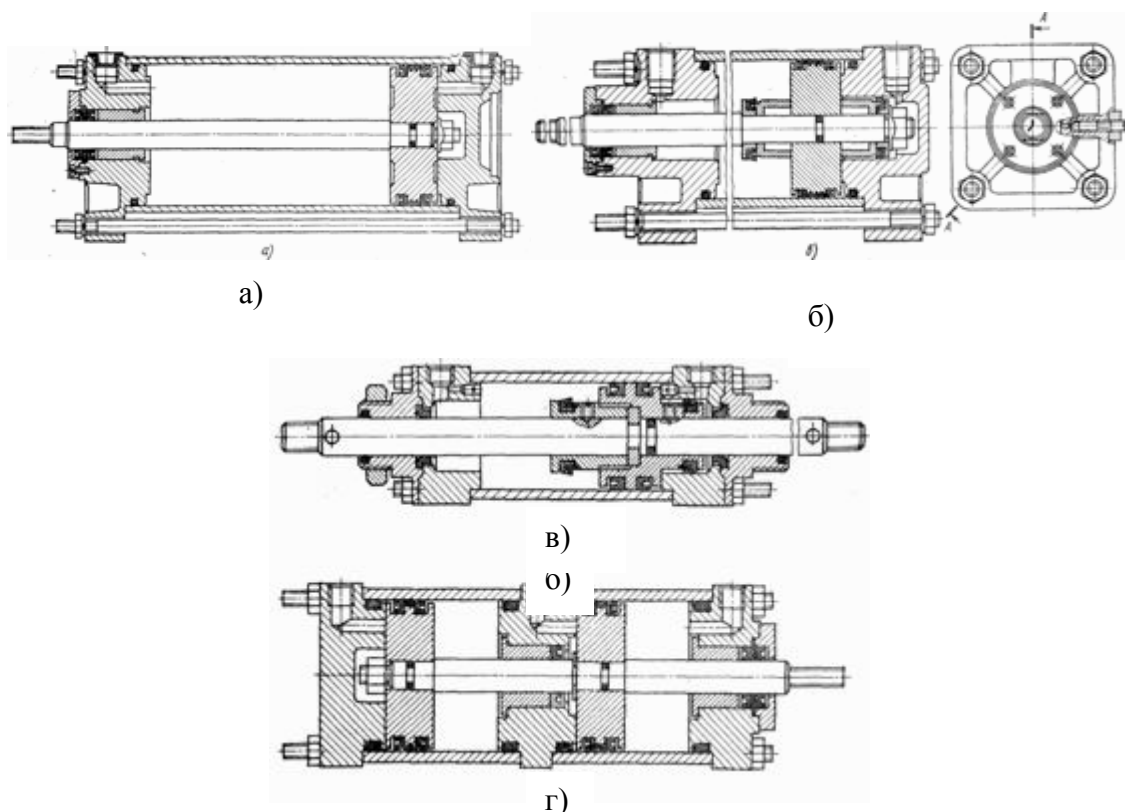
Пневмоцилиндры двухстороннего действия: а) без торможения;
